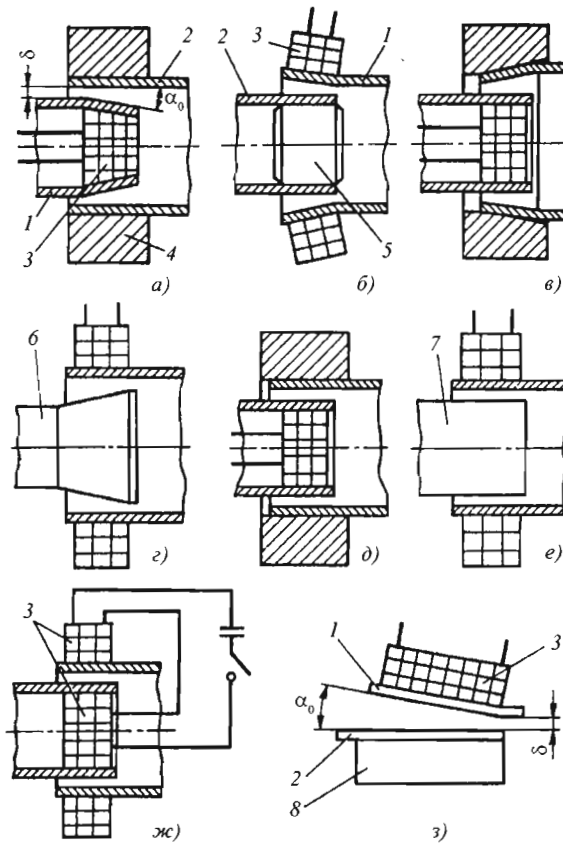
Схемы магнитно-импульсной сварки:
